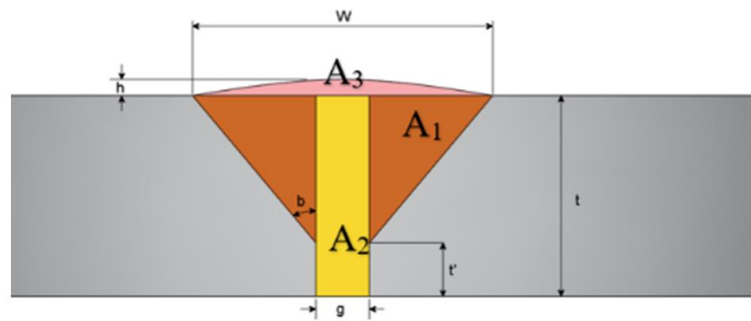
Desain las atau welding table lambung kapal Ferry Ro-Ro 1500 GT
